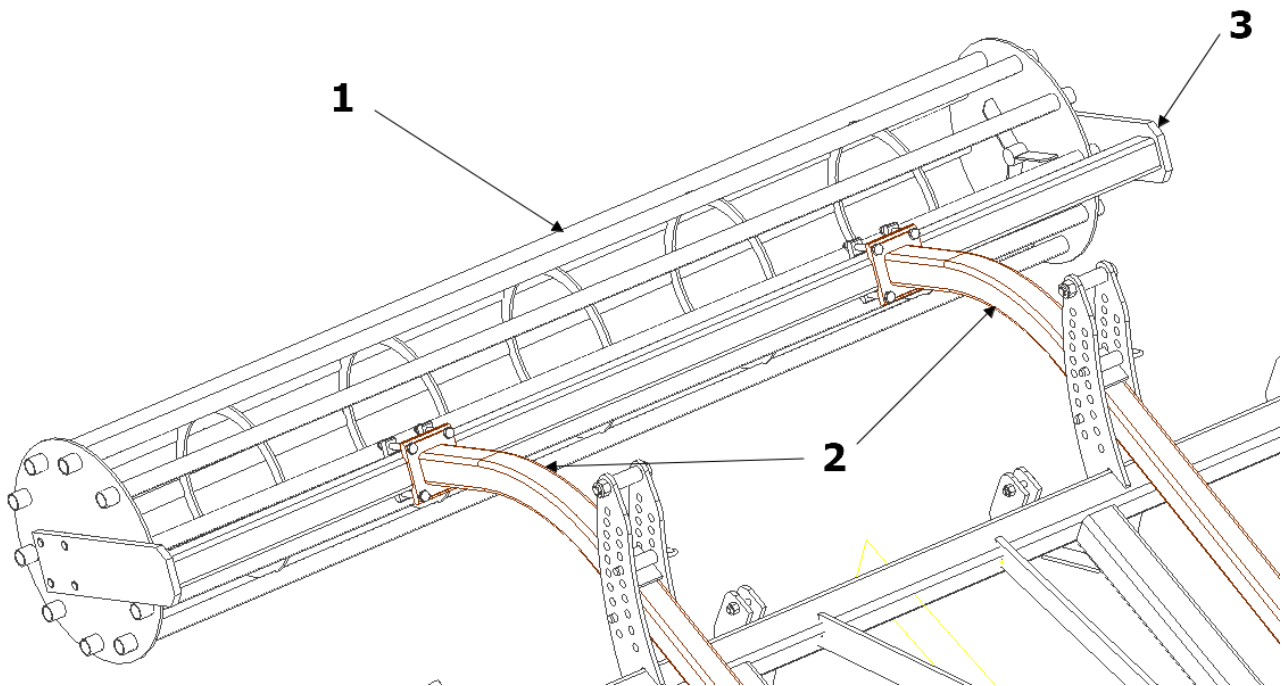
Verbindung der Arme mit der Halterung der Walze: 1 - Rohrwalze; 2 - Arme, 3 - Halterung der Walze.
